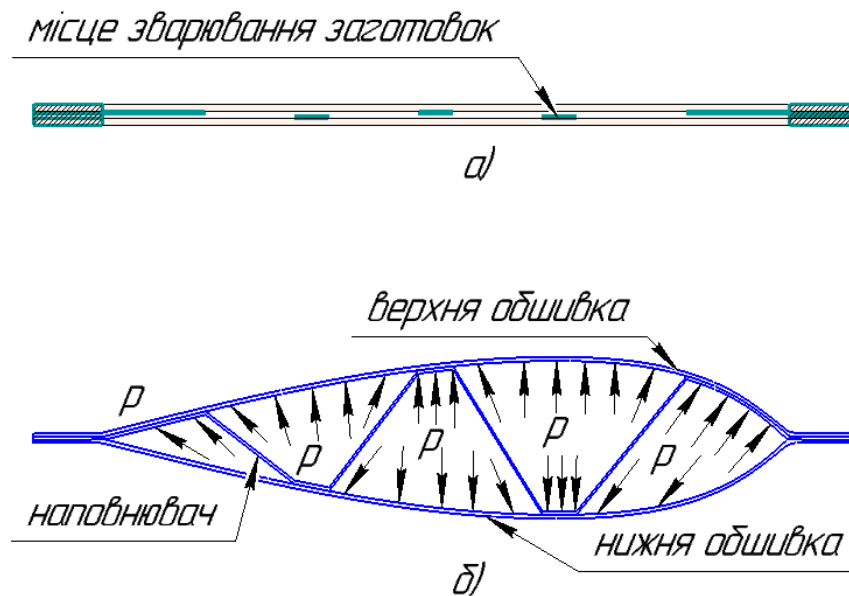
Схема з'єднання пакету заготовок та його формоутворення для розрахунку процесу: а – початковий пакет; б – деформація пакету під дією внутрішнього тиску
